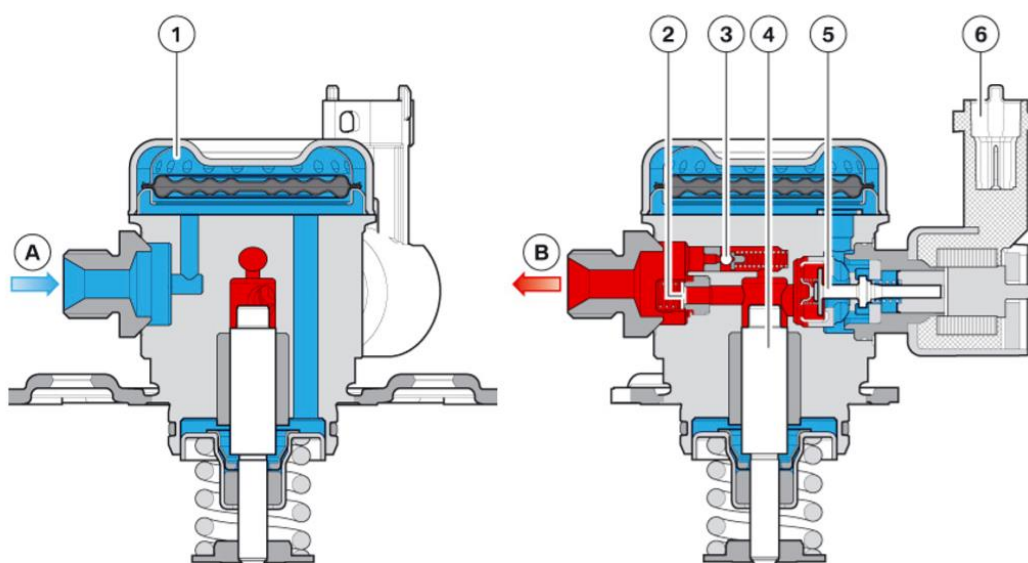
Řezy vysokotlakým čerpadlem Bosch HDP1 [27]
